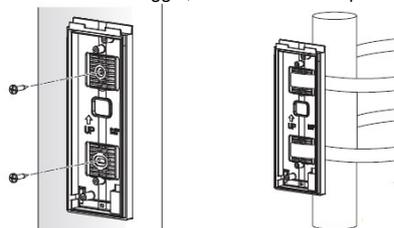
Montaggio del rilevatore. Montaggio standard e fissaggio mediante fascette di metallo.
